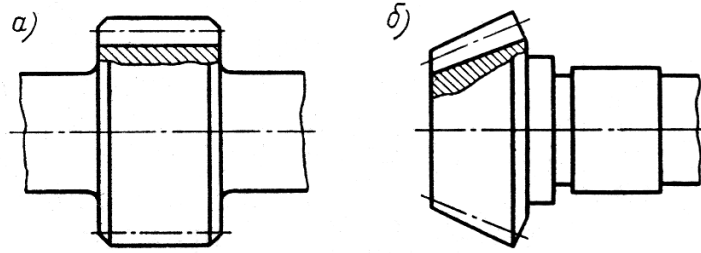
Конструкции вал-шестерен: *а* – цилиндрической; *б* – конической
